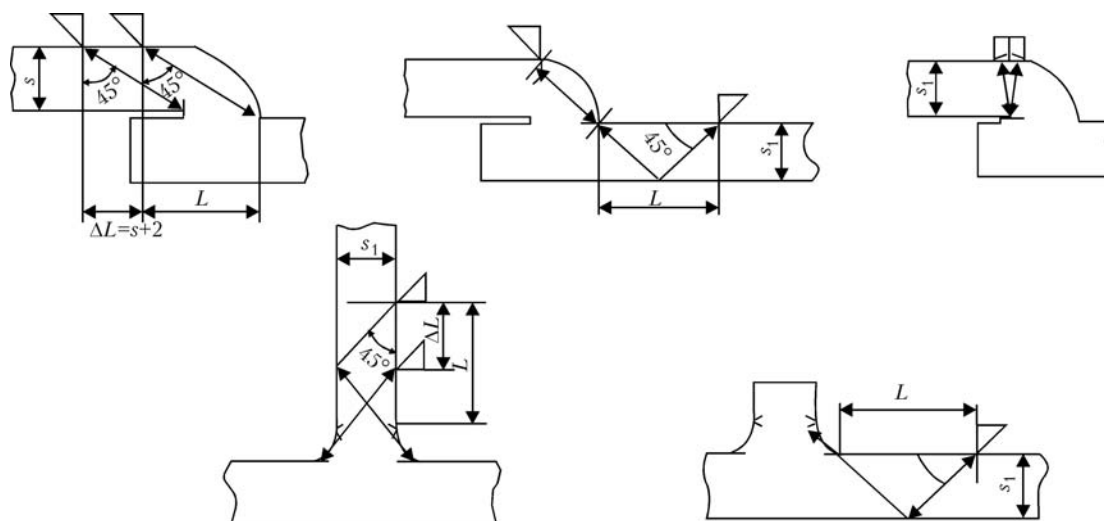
Схема ультразвукового контроля сварных соединений
